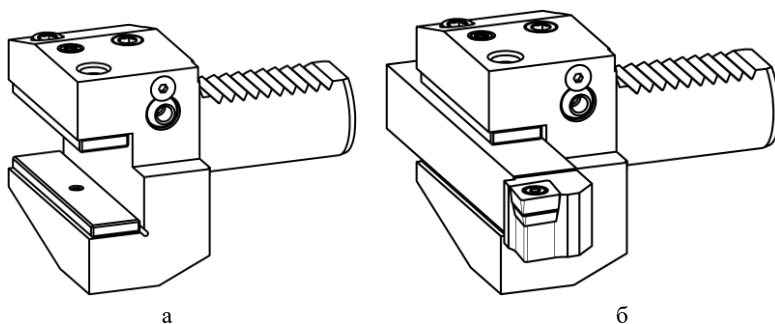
Резцедержатель для наружной обработки: а – без резца; б – с резцом
